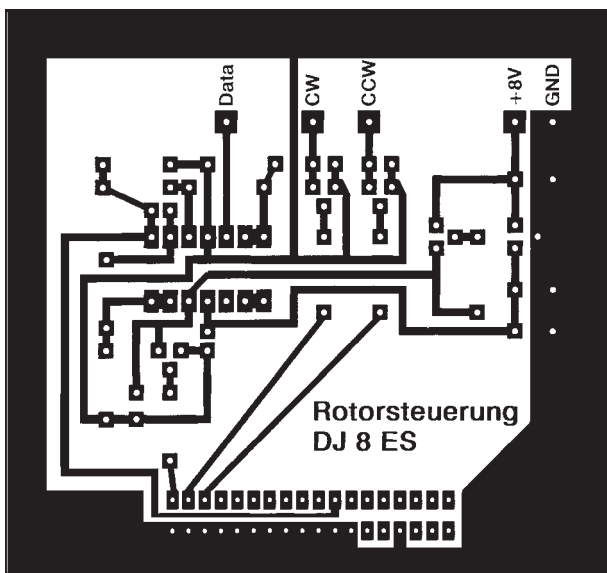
Leitungsführung der Platine für die Rotorsteuerung
